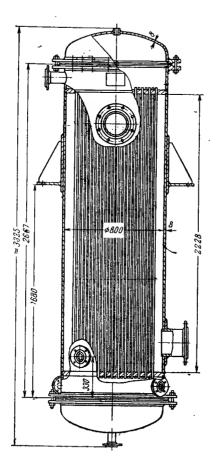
Вертикальный одноходовой дефлегматор с неподвижными трубными решетками.
